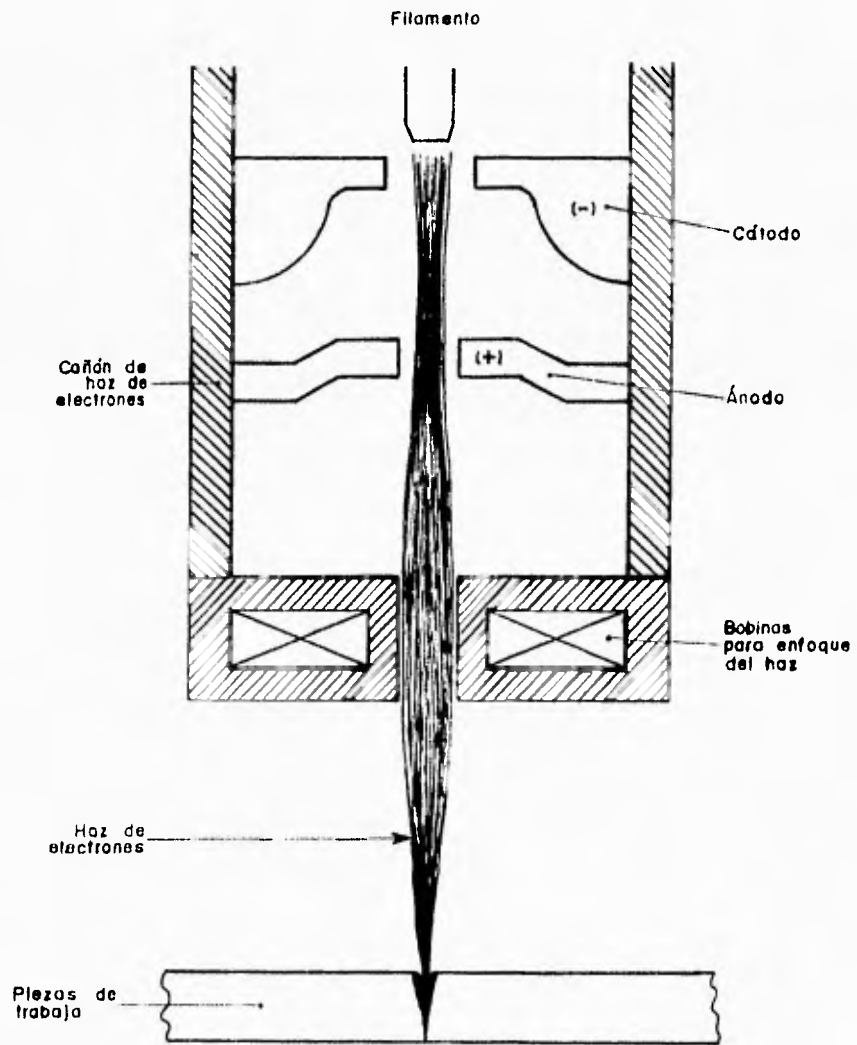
Soldadura por haz de electrones (EBW)
